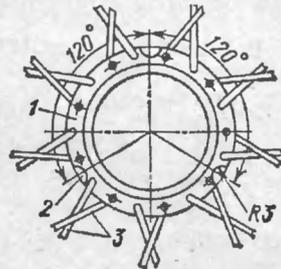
Место пропилов на буртике втулки для крепления большой звездочки с резиновыми прокладками:
